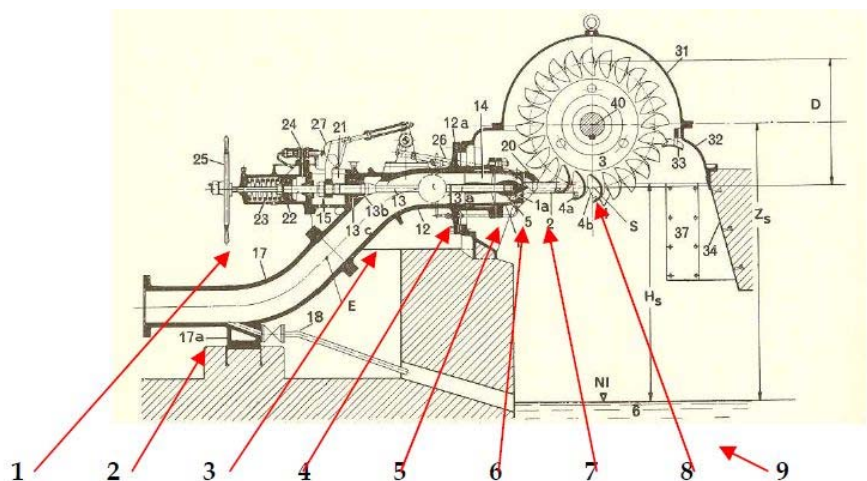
Componentes de una turbina Pelton de eje horizontal.
